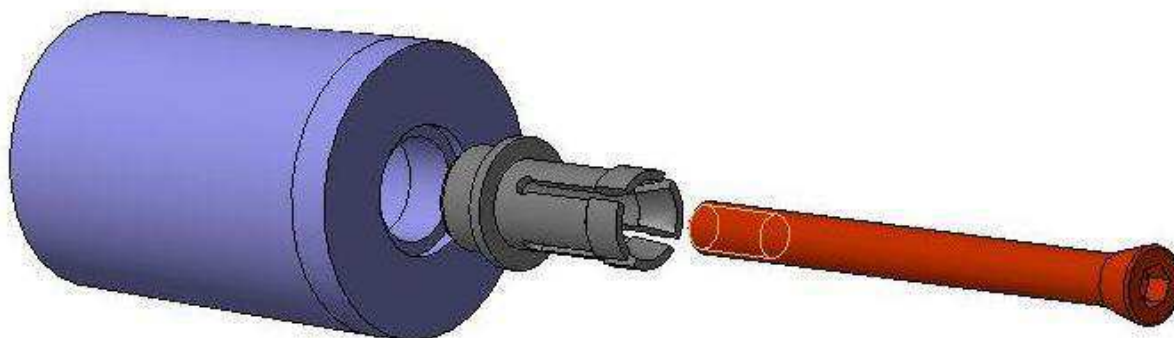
Разнесение 3D модели токарного приспособления на детали
